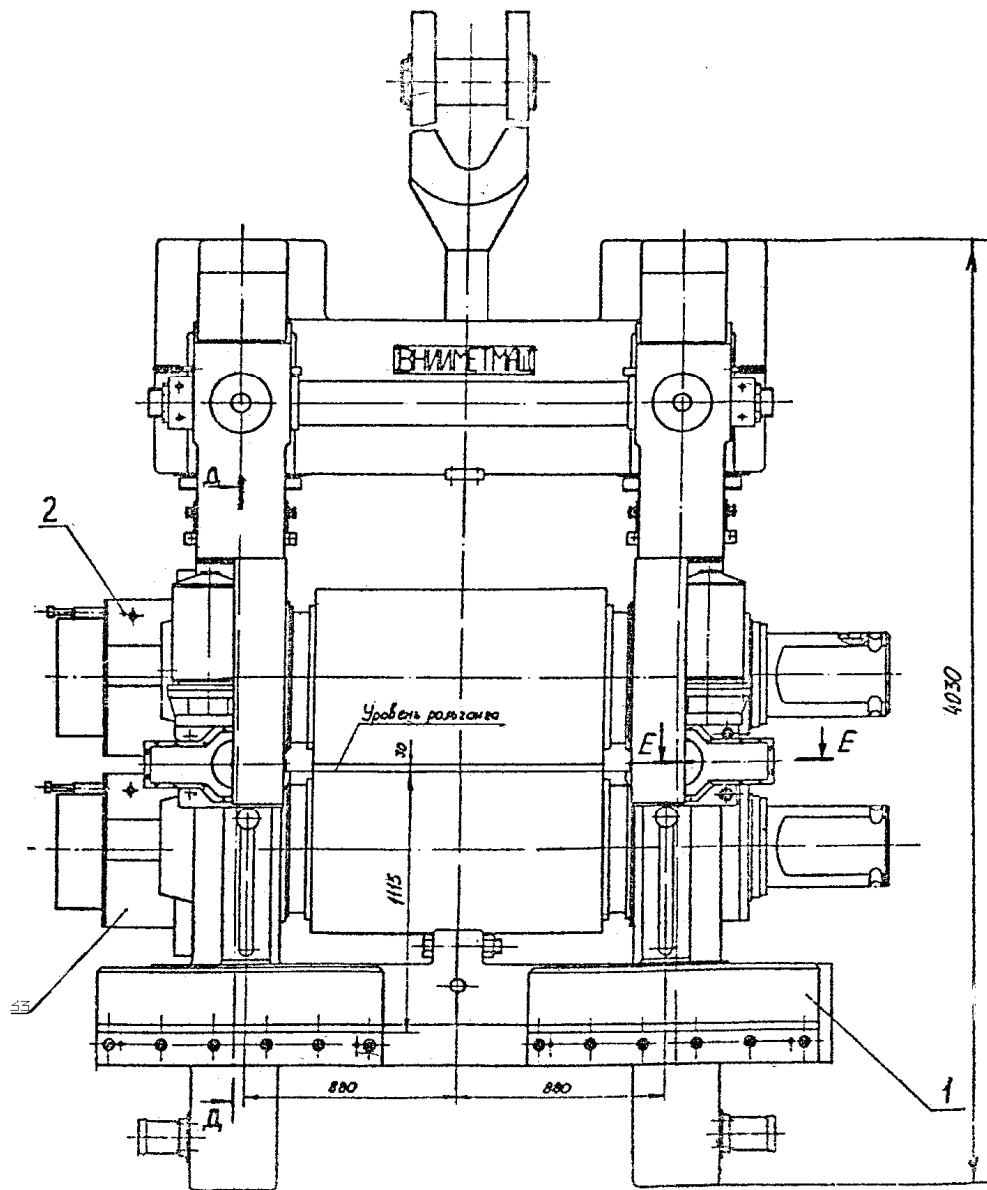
Кліть 730 ПН. Загальний вид (вид з переду)
